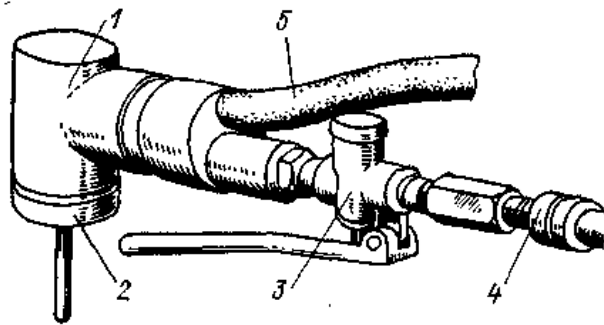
Электрододержатель для подводной кислородно-дуговой резки (сварки): 1-головка, 2-зажимной патрон, 3-клапан, 4-подвод кислорода, 5-кабель
